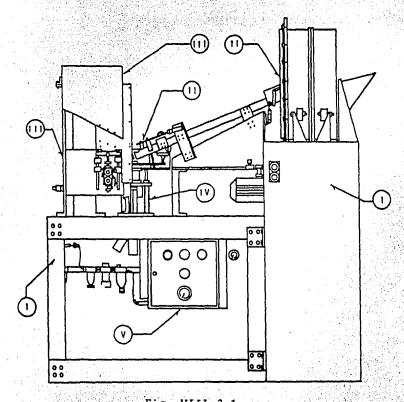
Configuración general de la máquina ensambladora de tuercas y tornillos
